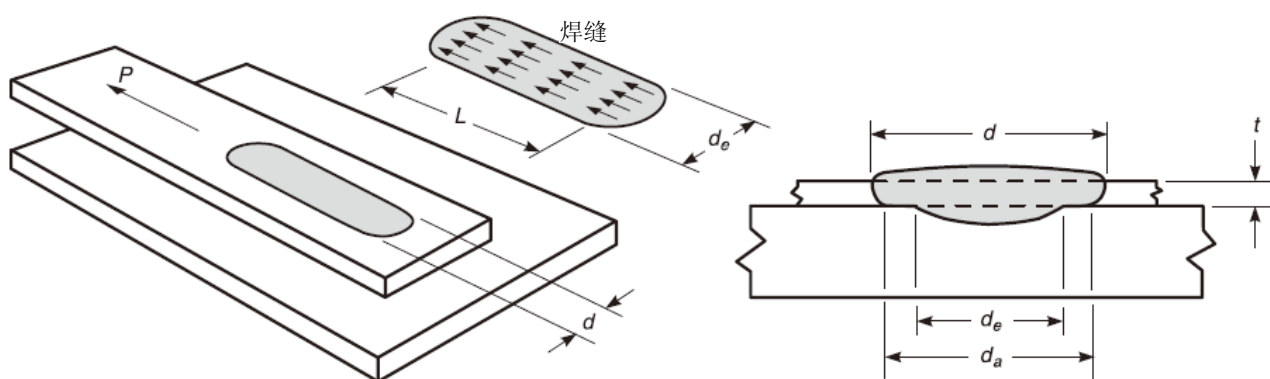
支撑板中的电弧缝焊缝
